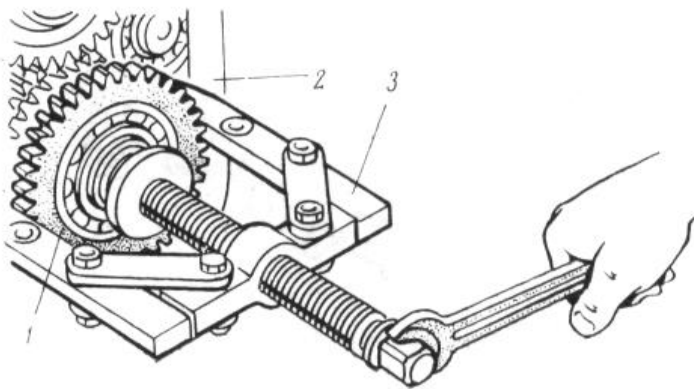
Випресування проміжної шестерні понижаючого редуктора: 1- шестерня; 2- корпус коробки передач; 3- знімач.
